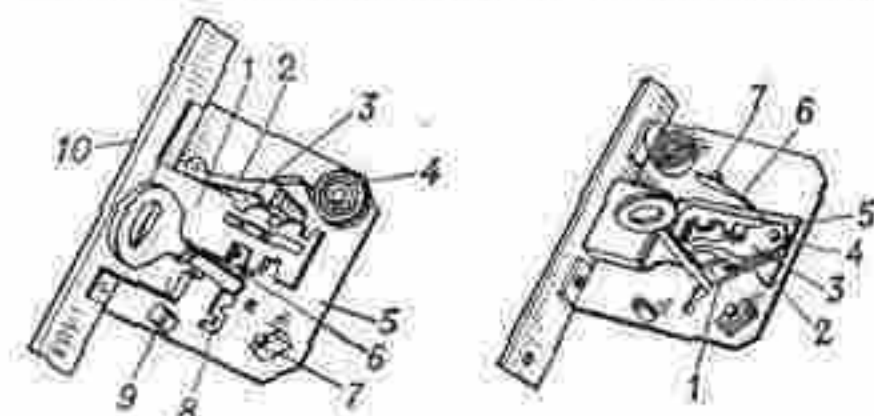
(слева). Бессувальдный замок с ключом: 1 — ригель (засов); 2 — собачка; 3 — запорный паз; 4 — пружина собачки; 5 — основание корпуса; 6 — бороздка ключа; 7 — распорная стойка; 8 — ключевина; 9 — стойка крепления; 10 — лицевая планка. Рис. 2 (справа). Двухоборотный сувальдный замок с ключом: 1 — бороздка ключа с прорезями для сувальд; 2 — ригель; 3 — сувальда с прорезкой под запорную стойку; 4 — ось; 5 — запорная стойка; 6 — пружина сувальды; 7 — упорный штифт.
